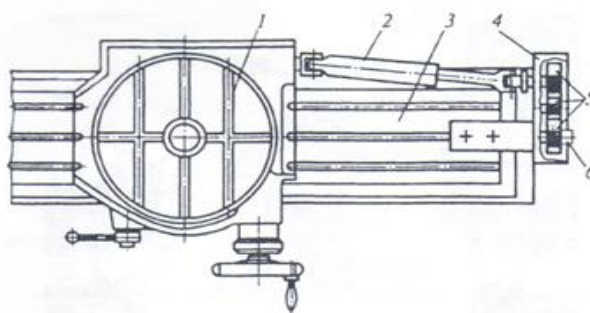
Круглый поворотный стол с приводом от механизма подачи фрезерного станка:
